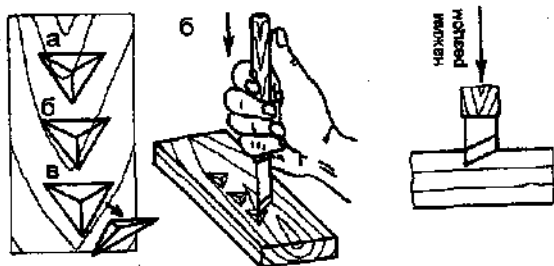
Выполнение трехгранно-выемчатой резьбы: а — разметка; б — накальвание; в — подрезка
